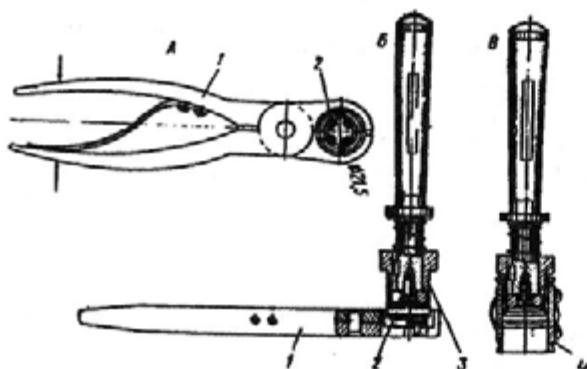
Установка пружинного кольца автоматического устройства в колесный цилиндр:
